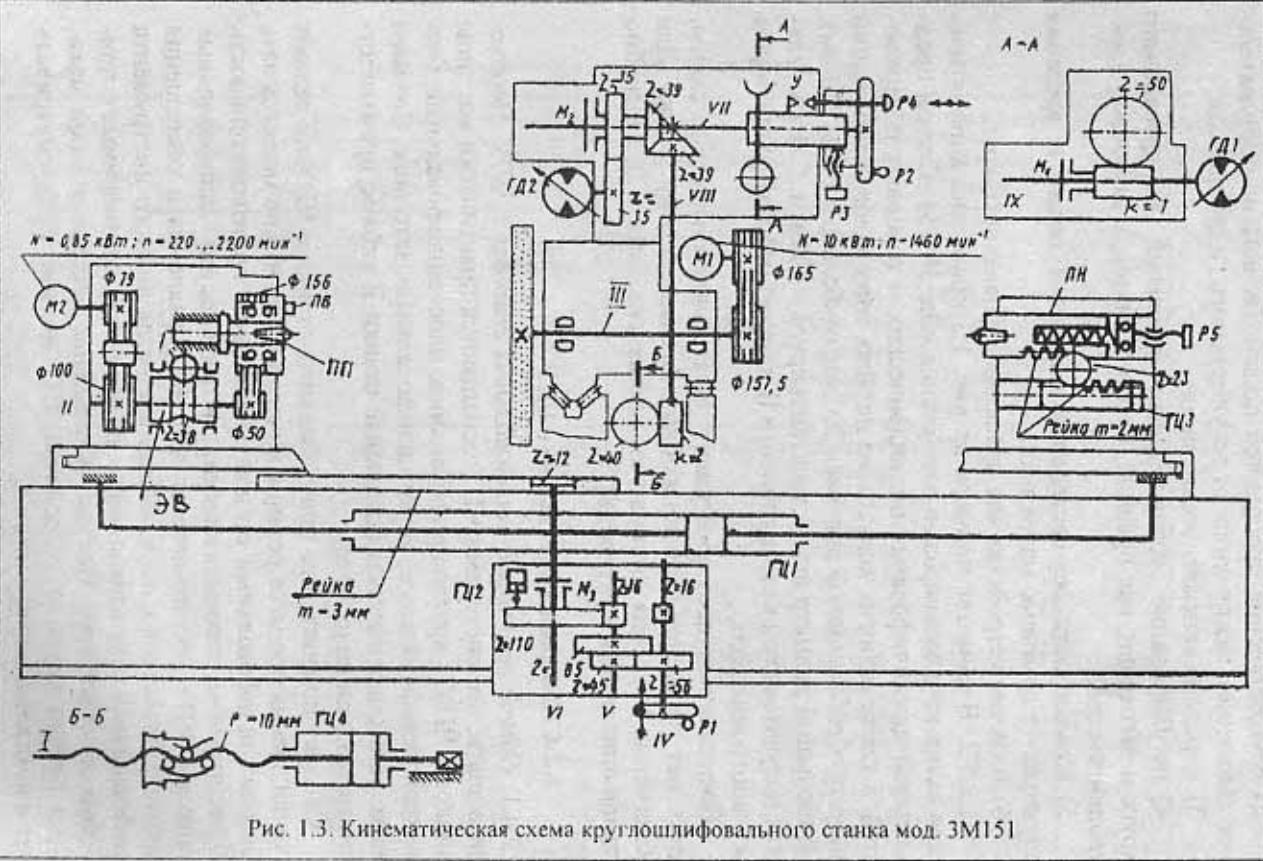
Кинематическая схема круглошлифовального станка мод. 3М151
